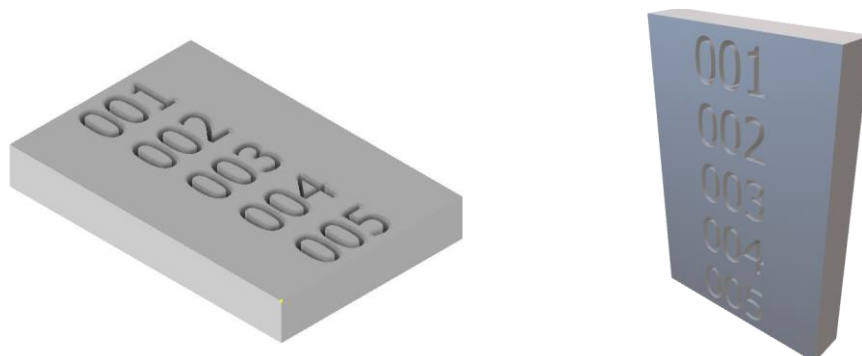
Τρισδιάστατη απεικόνιση αποστολής 36
